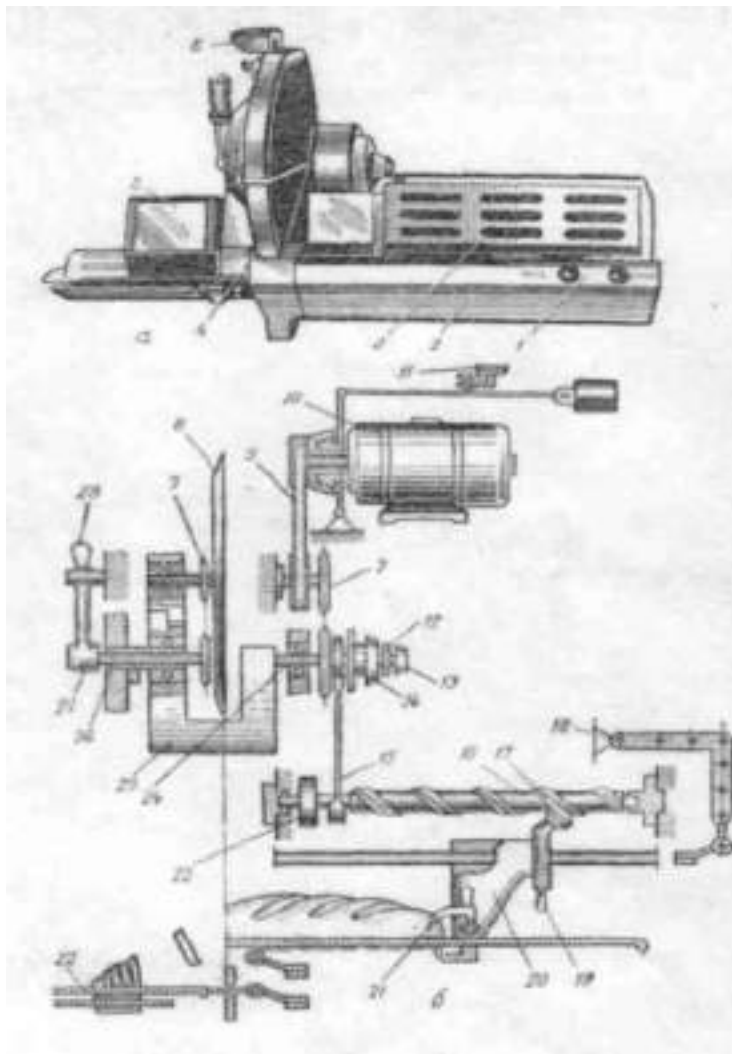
Хлеборезательная машина МРХ-200: а - общий вид: 1 - кнопочный выключатель; 2 - чугунная станина; 3 - загрузочный лоток; 4 - кожух; 5 -откидной щиток; 6 - механизм заточки ножа; б - кинематическая схема: 7 -звездочка; 8 - нож; 9 - ременная передача; 10 - электродвигатель; 11 - рукоятка растормаживания; 12 - стопорный диск; 13 - гайка; 14 - диск с делениями; 15 -шатун; 16 - ходовой вал; 11 - ролик; 18 - предохранительная решетка; 19 - ручка; 20 - каретка; 21 - захват; 22 - приемный лоток; 23 - муфта свободного хода; 24 -приводной вал; 25 - противовес; 26- втулка; 27 - рычаг, 28–рукоятка.
